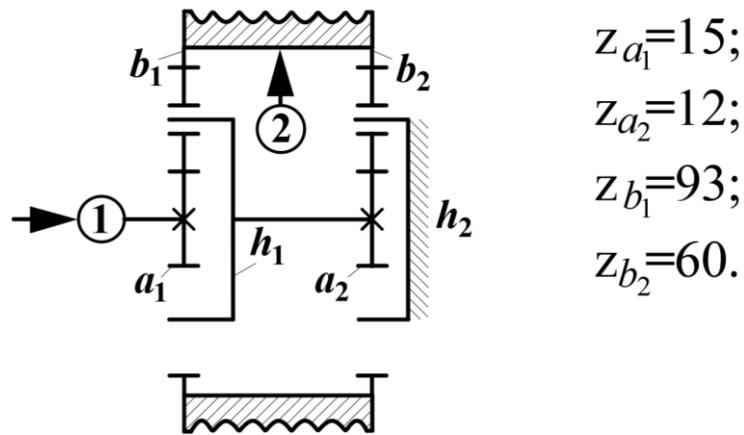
Схема редуктора механизма подъема главной лебедки экскаватора Э-6516
